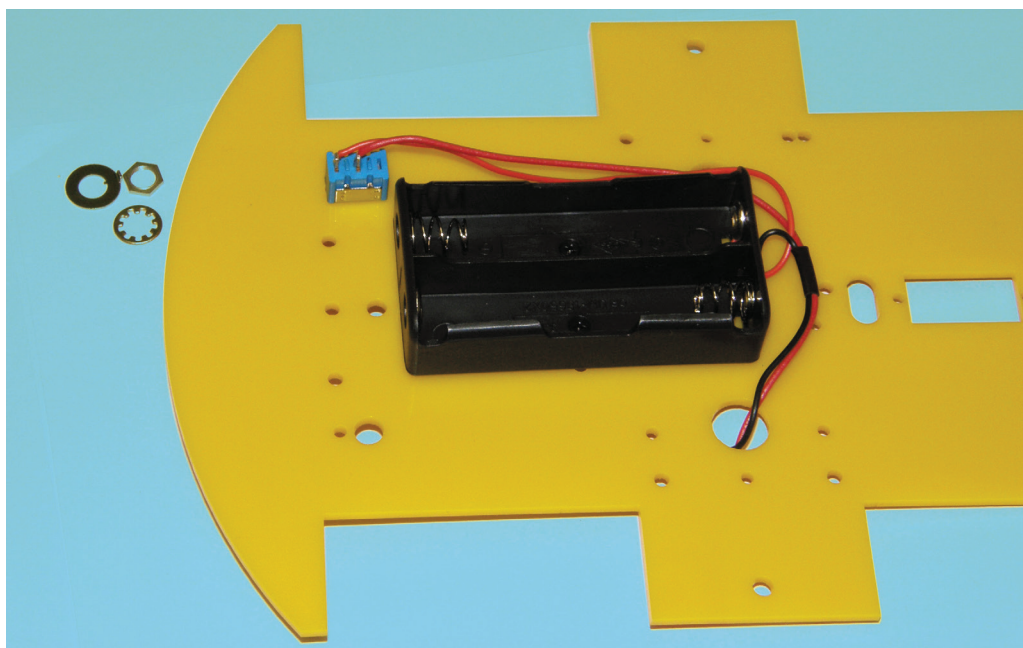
Выключатель установлен в отверстие корпуса (вид снизу)
